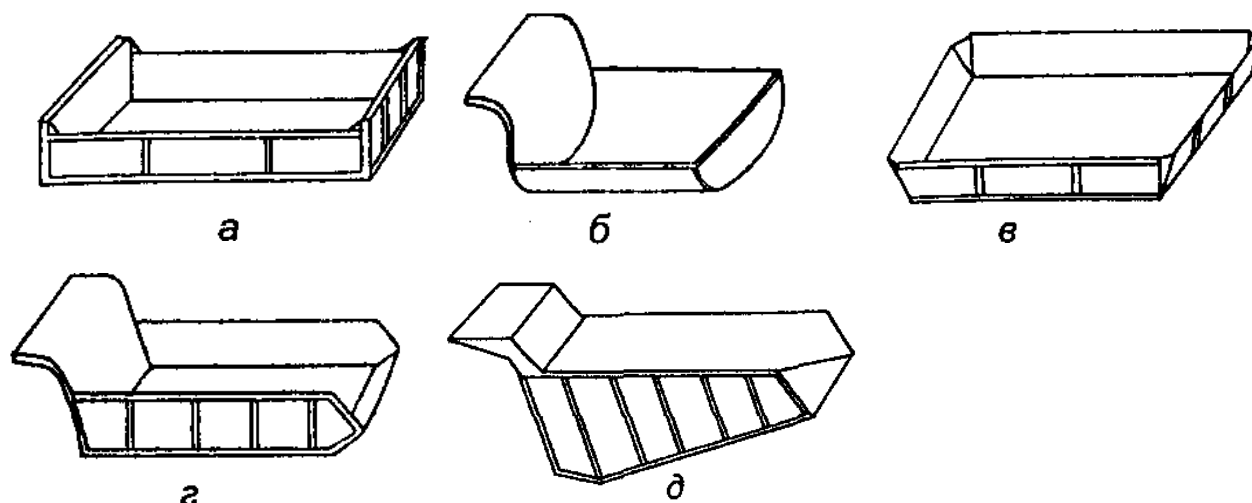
Формы кузовов автомобилей-самосвалов: а – прямоугольный; б – полуэллиптический; в – корытообразный; г – ковшовый; д – совковый
